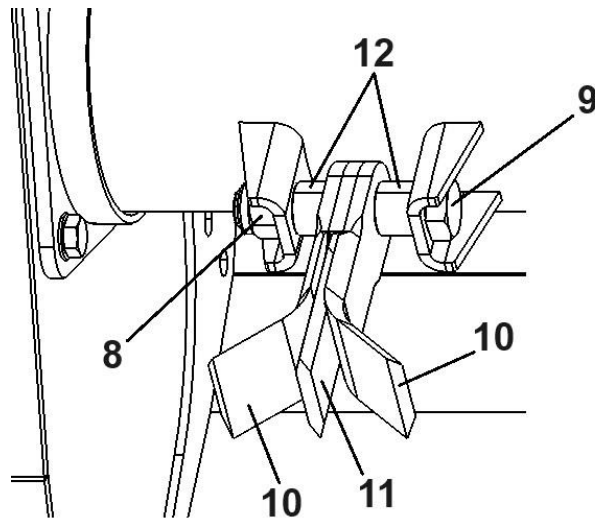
Auswechseln der Schneidmesser: 8 – Befestigungsmutter, 9 – Befestigungsschraube, 10 – „Y“-Messer, 11 – gerades Messer, 12 – Buchse
